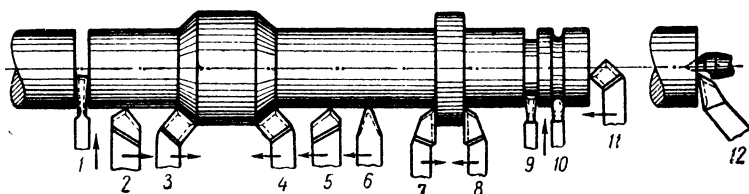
Основные виды токарных резцов для наружного обтачивания:
